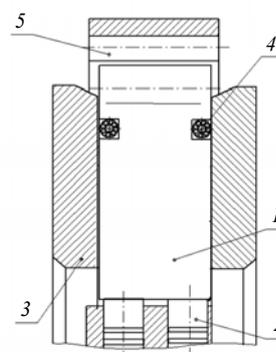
Конструкция передачи с гибким элементом в виде тросов: 1 – плунжер; 2 – поршень волнообразователя; 3 – сепаратор; 4 – металлические тросы; 5 – зубчатое колесо
